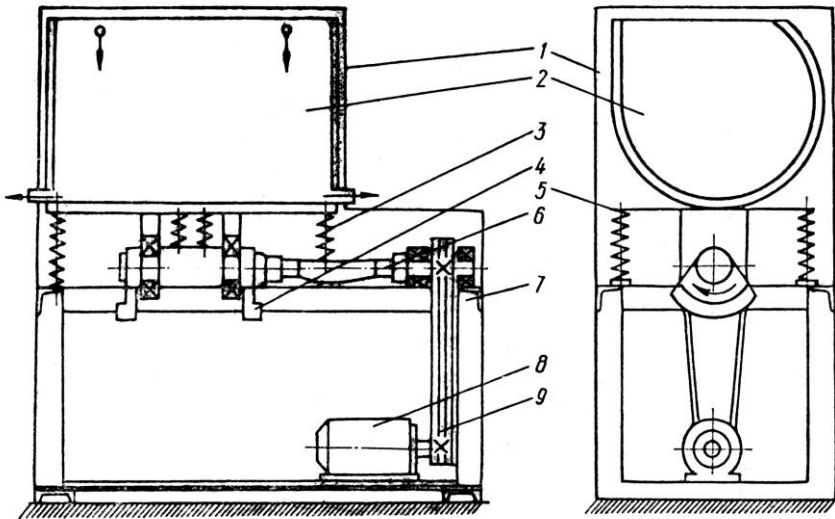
Установка віброабразивного очищення: 1 – захисний кожух; 2 – V-подібний контейнер з миючим середовищем; 3 – пружина; 4 – дебалансний вібратор; 5 – вібрувальна платформа; 6 – гнучкий вал; 7 – станина; 8 – електричний двигун; 9 – клинопасова передача
